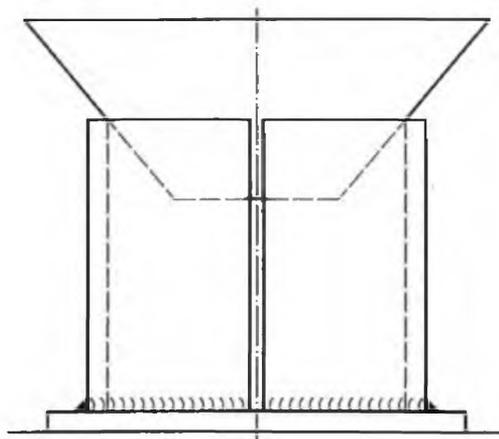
Подготовка и испытание на излом образцов угловых швов труб
